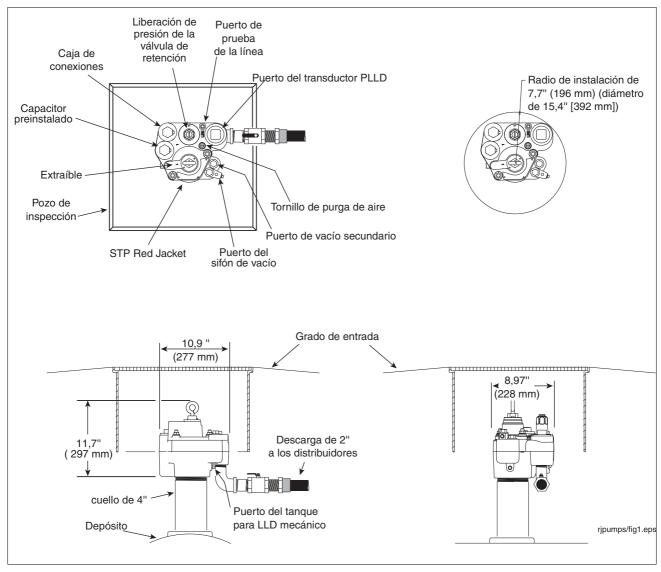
Componentes y dimensiones del pac/man Red Jacket
